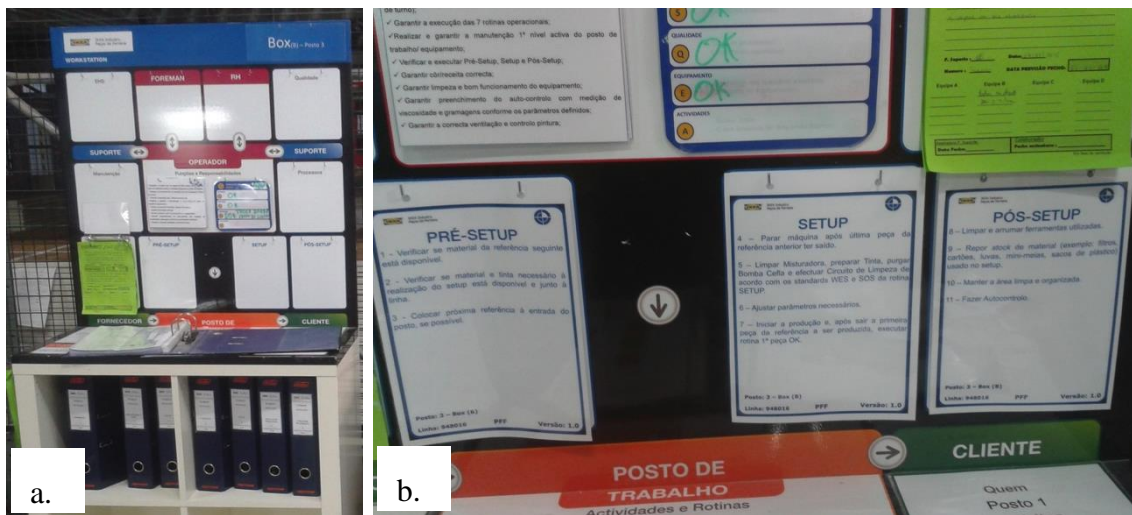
Workstation* do Posto 3 (*Box* de Pintura) da L16: a) Antes de serem colocadas as folhas de Instrução. b) Depois de serem colocadas as folhas de instrução “Pré-Setup”, “Setup” e “Pós-Setup”.
